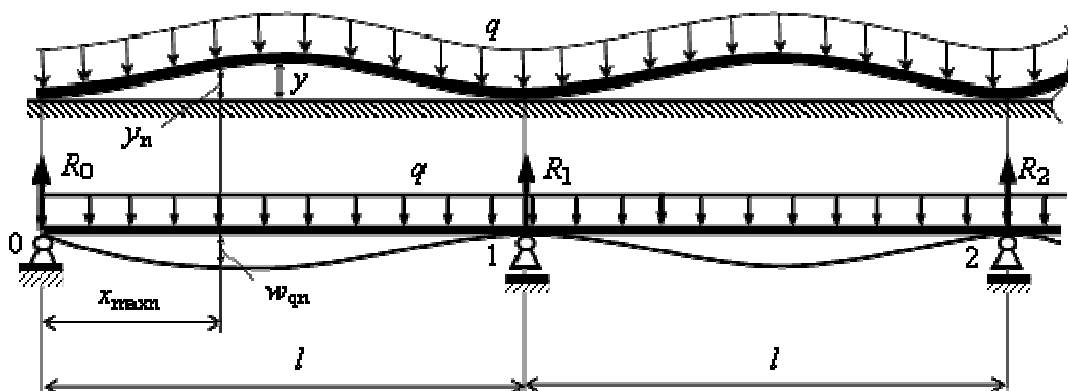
Расчетная схема заготовки при закреплении магнитным полем стола
